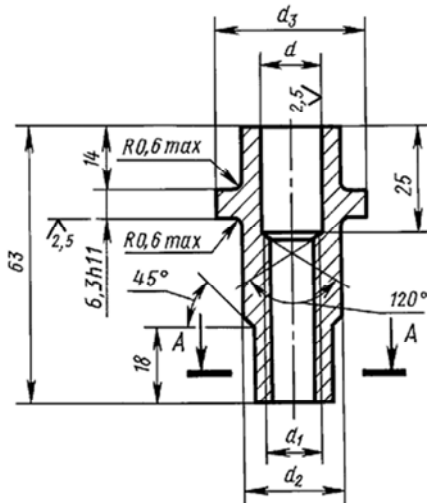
Конструкция втулки регулируемого выталкивателя
